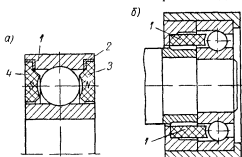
Шарикоподшипники с магнитными сепараторами
